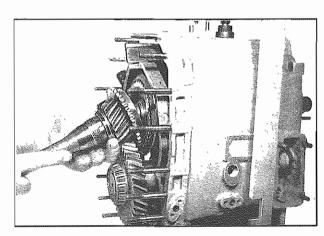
Spingere l'albero presa diretta sulla gabbia a denti Push slide main shaft over gear cage
